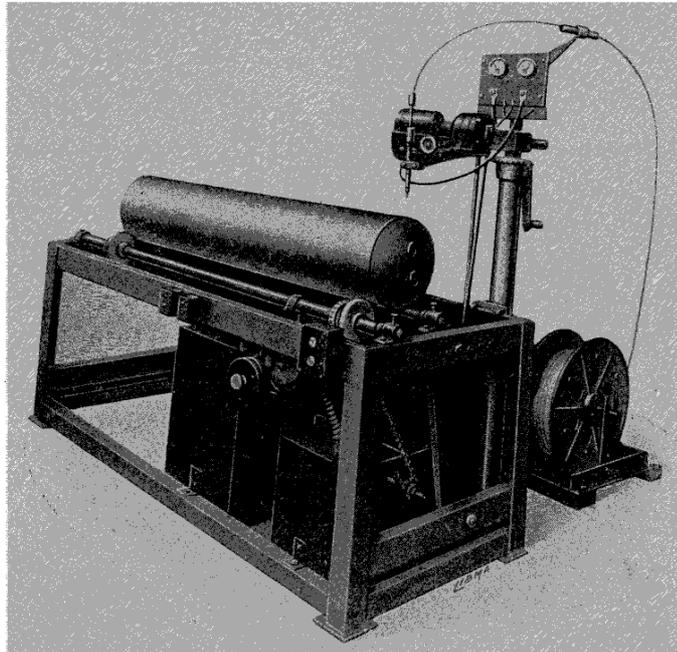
Machine automatique pour la soudure des fonds de réservoirs.
